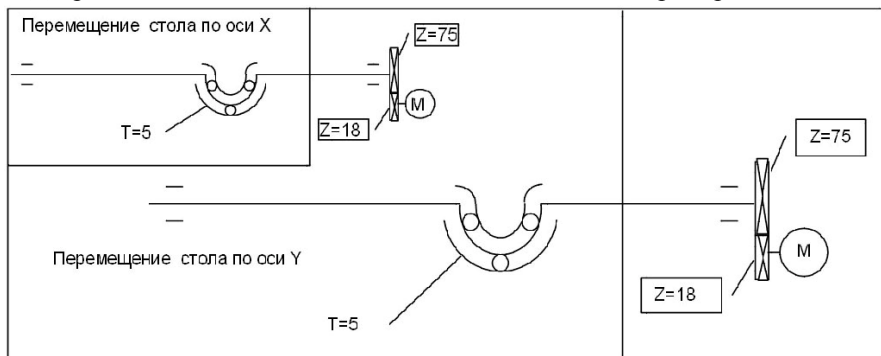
Схема кинематическая привода рабочего станка КД46.
